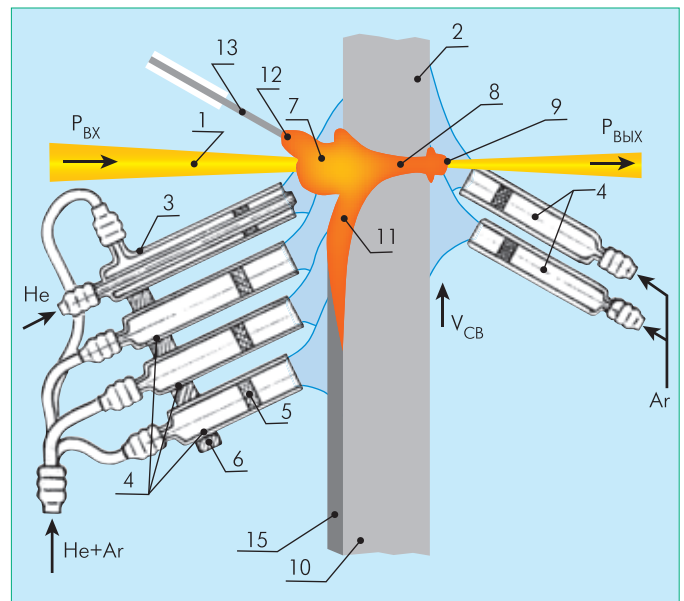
Схема лазерной и лазерно-дуговой сварки излучением до 10–30 кВт, разработана авторами [11, 19]: 1 – лазерный пучок, 2 – свариваемое изделие, 3 – защитное комбинированное цилиндрическое сопло для подачи гелия и гелиево-аргоновой смеси, 4 – защитные цилиндрические сопла для подачи гелиево-аргоновой смеси и Ar, 5 – пористые керамические вставки-рассекатели, 6 – кронштейн для крепления сопел, 7 – плазменный факел с лицевой стороны шва, 8 – "плазменная шуба" внутри парагазового канала, 9 – плазменный факел с наружной стороны шва (в случае защиты ее аргоном), 10 – сварочная ванна, 12 – сварочная дуга (в случае использования ее для лазерно-дуговой сварки), 13 – плавящийся (или неплавящийся) электрод, 15 – усиление сварного шва
